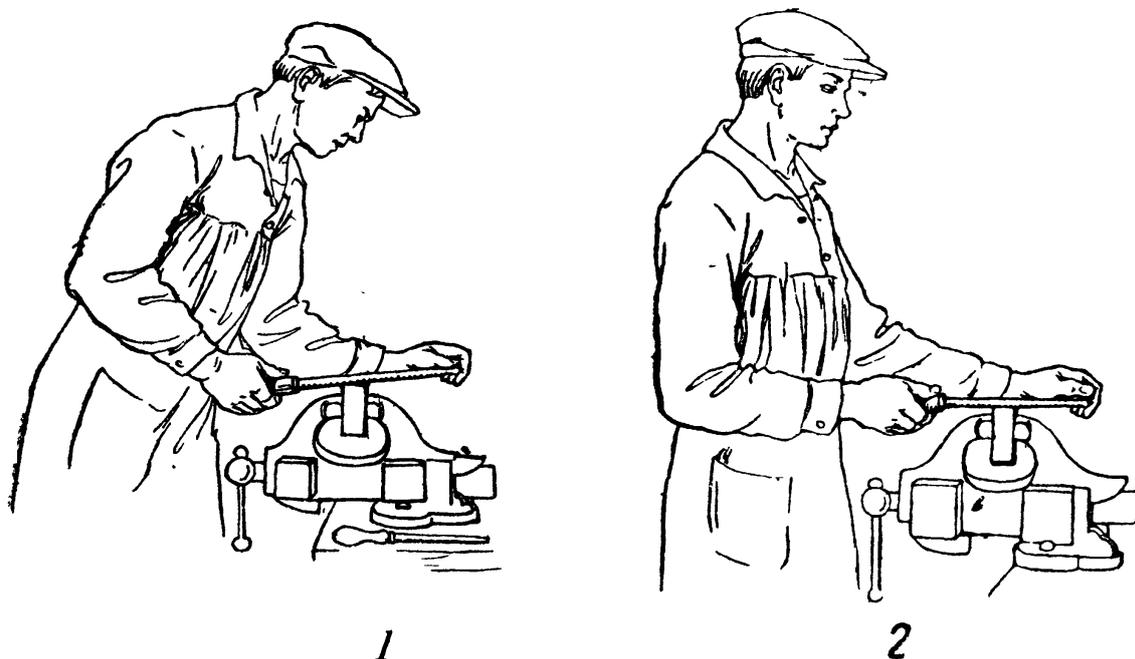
Положение корпуса при опиловке: 1 — неправильное; 2 — правильное
